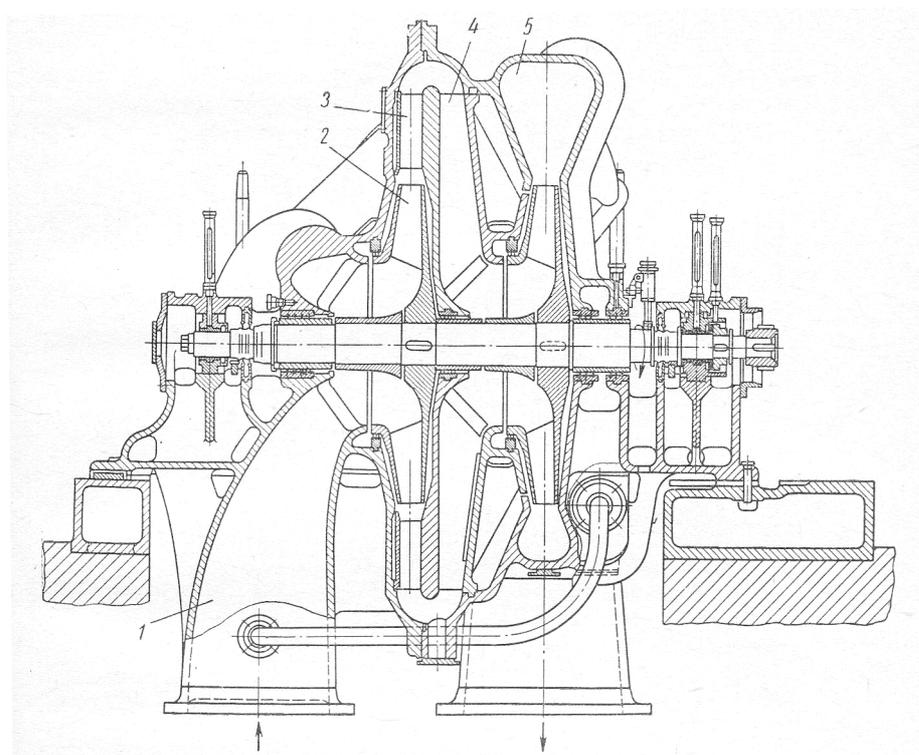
Двухступенчатый центробежный компрессор:
